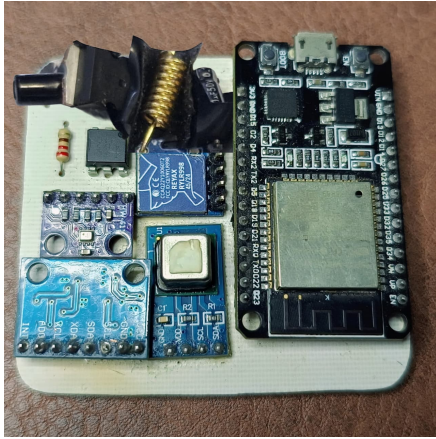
PCB del sistema de control del CanSat completamente ensamblada.
